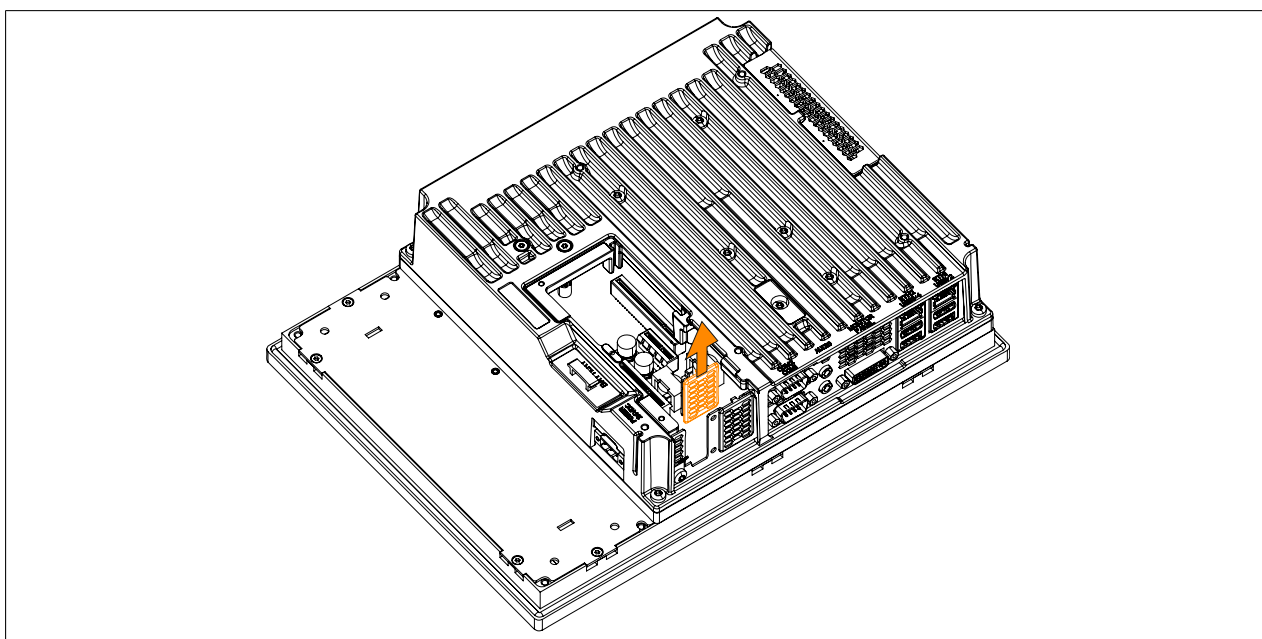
Torxschrauben und Blindabdeckung entfernen
